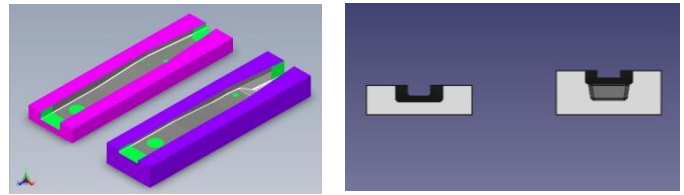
CAD del molde desmontable para la fabricación del basculante.
